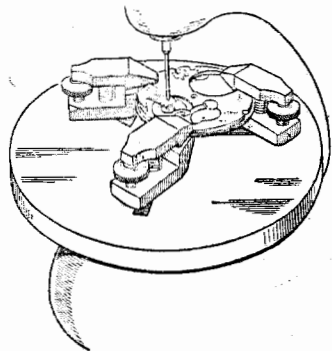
Цилиндрическая часть развертки в отверстии опоры.
